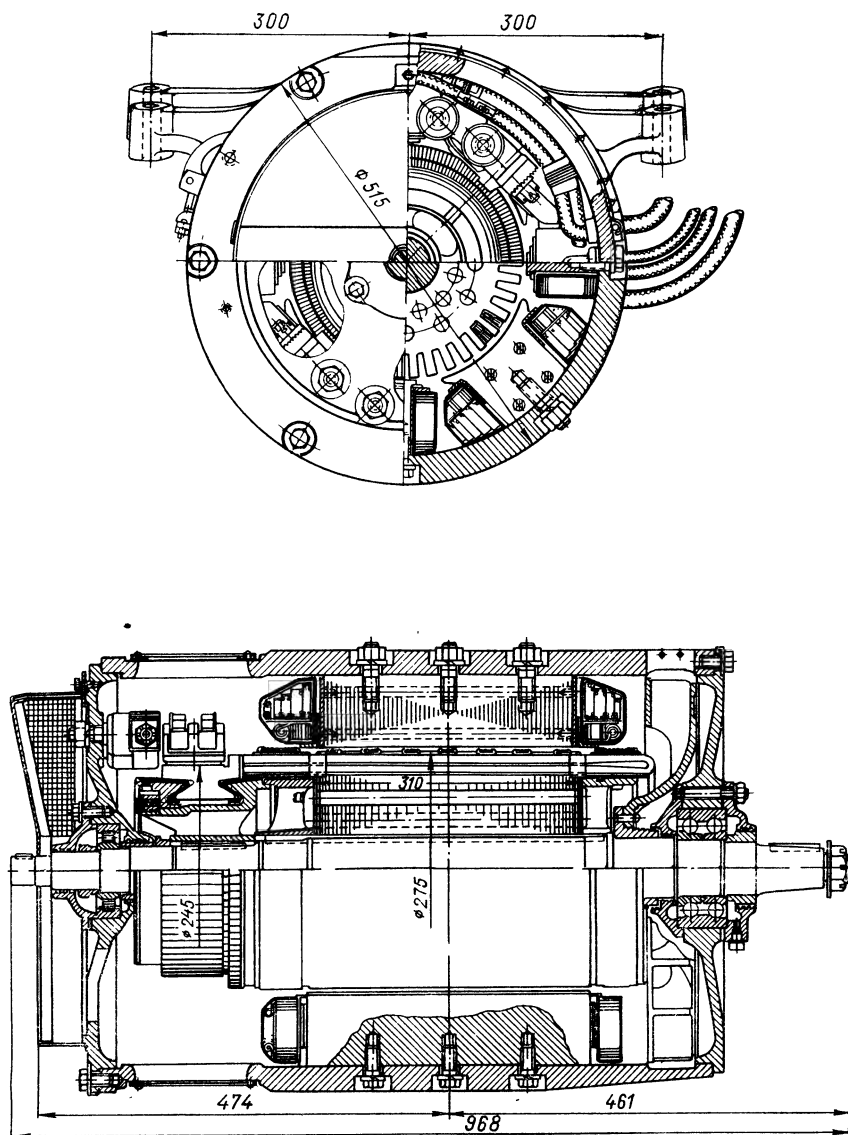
Троллейбусный двигатель ДК-202 с цилиндрической станиной
